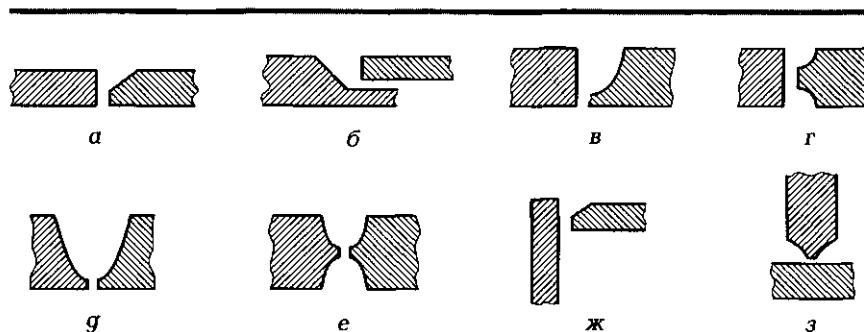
Формы кромок, подготовленных под сварку:
